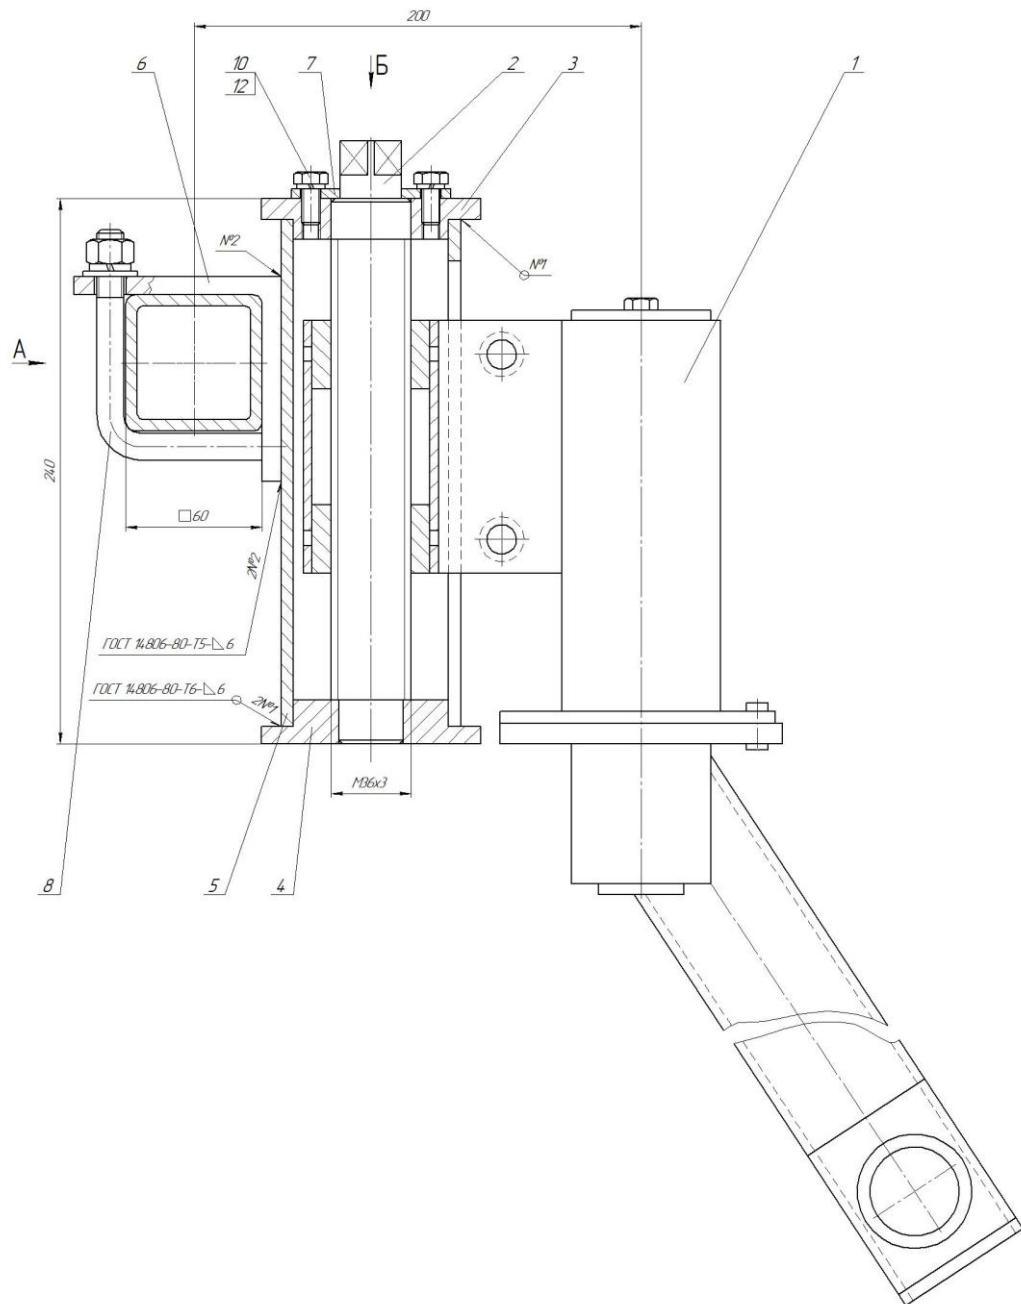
Схема гвинтового механізму опорного колеса:
